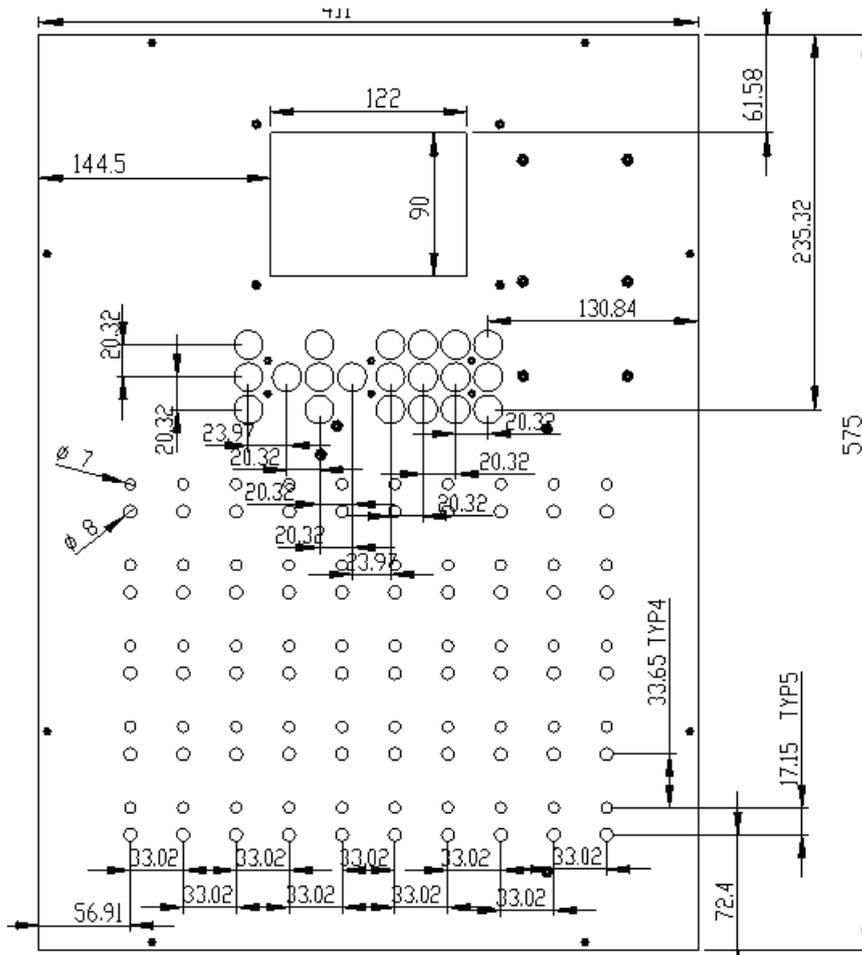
Dimensioni del Pannello Anteriore di Platinum Pro 50
